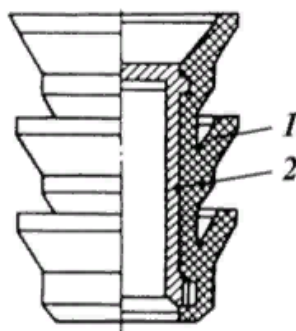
1-резиновая манжета; 2-алюминиевый корпус.
